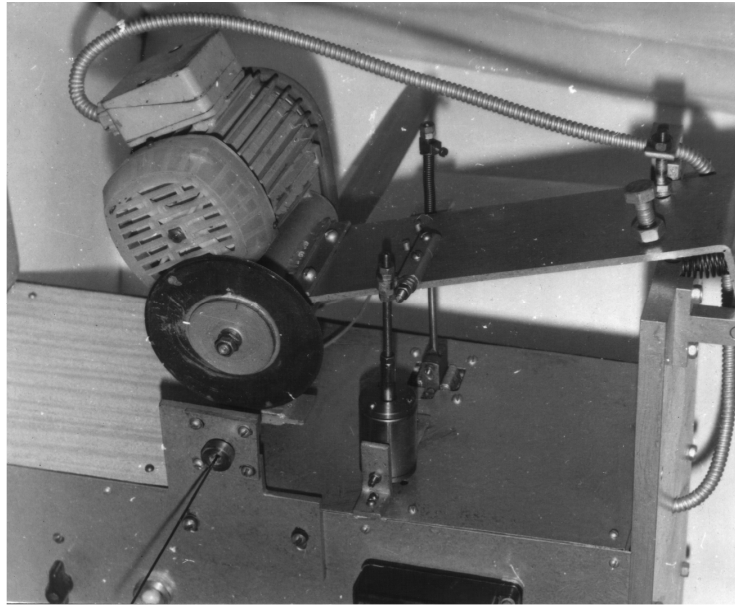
Устройство порезки стержня со снятым защитным кожухом
